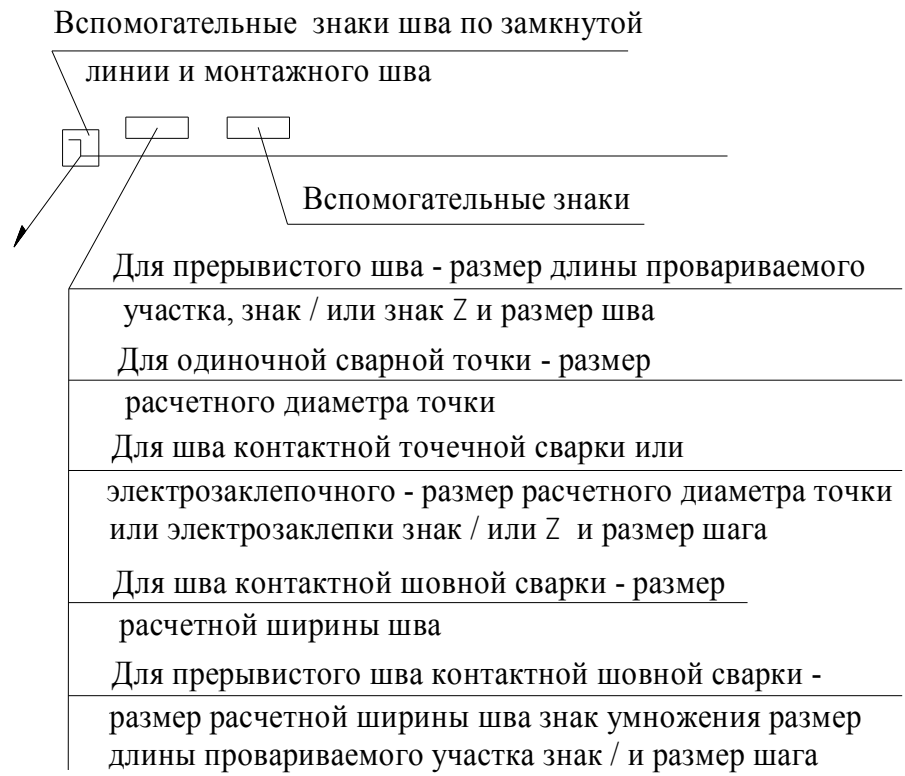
Структура обозначения нестандартного шва или одиночной точки
